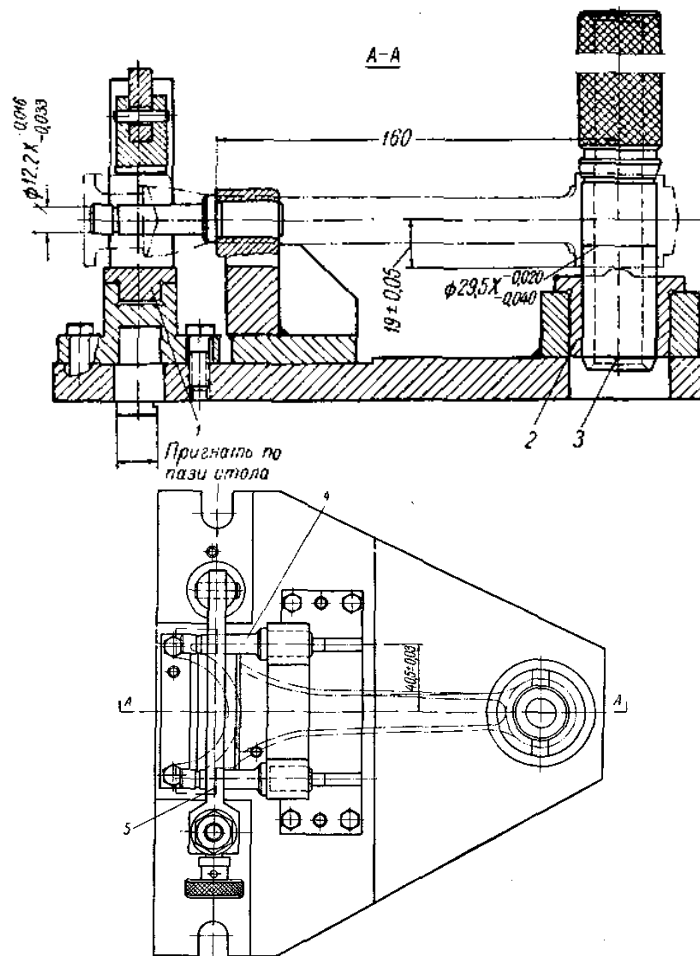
Приспособление для фрезерования торцов разъема нижней головки шатуна.
